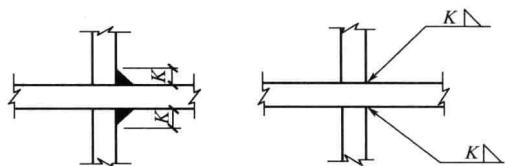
3个及3个以上焊件的焊缝标注方法
